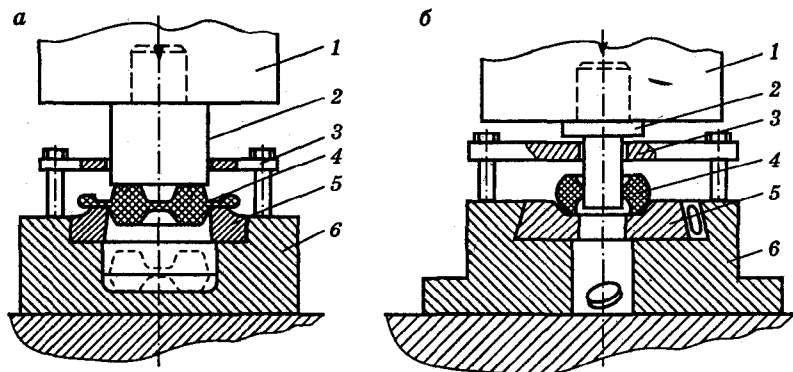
Схема обрезки облоя (а) и пробивки отверстий (б)
